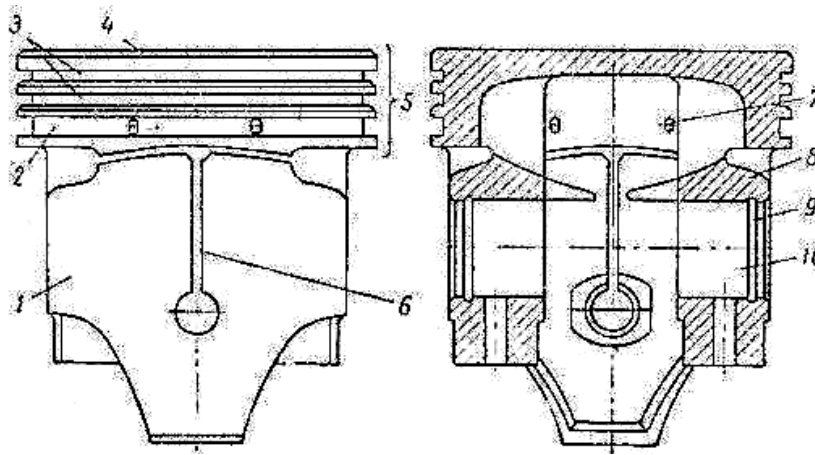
Поршень в разрезе: 1 – юбка поршня; 2 – канавка маслосъемного кольца; 3 – канавки компрессионных колец; 4 – днище поршня; 5 – головка поршня; 6 – тепловой разрез юбки; 7 – маслоотводящее отверстие; 8 – бобышка; 9 – стопорная канавка; 10 – отверстие под палец
